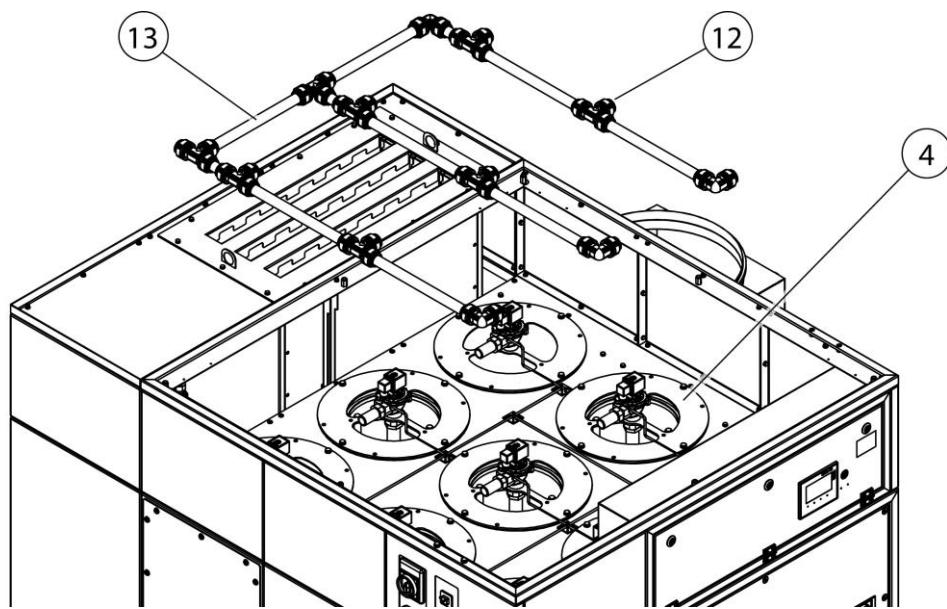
Remplacement du filtre – Démontage de la tuyauterie d'air comprimé
